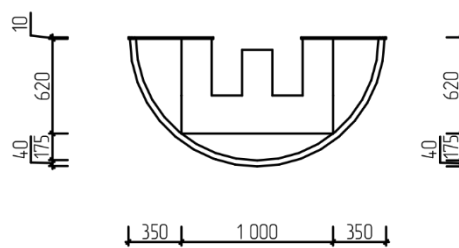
Чертеж оборудования. Вид прямо
